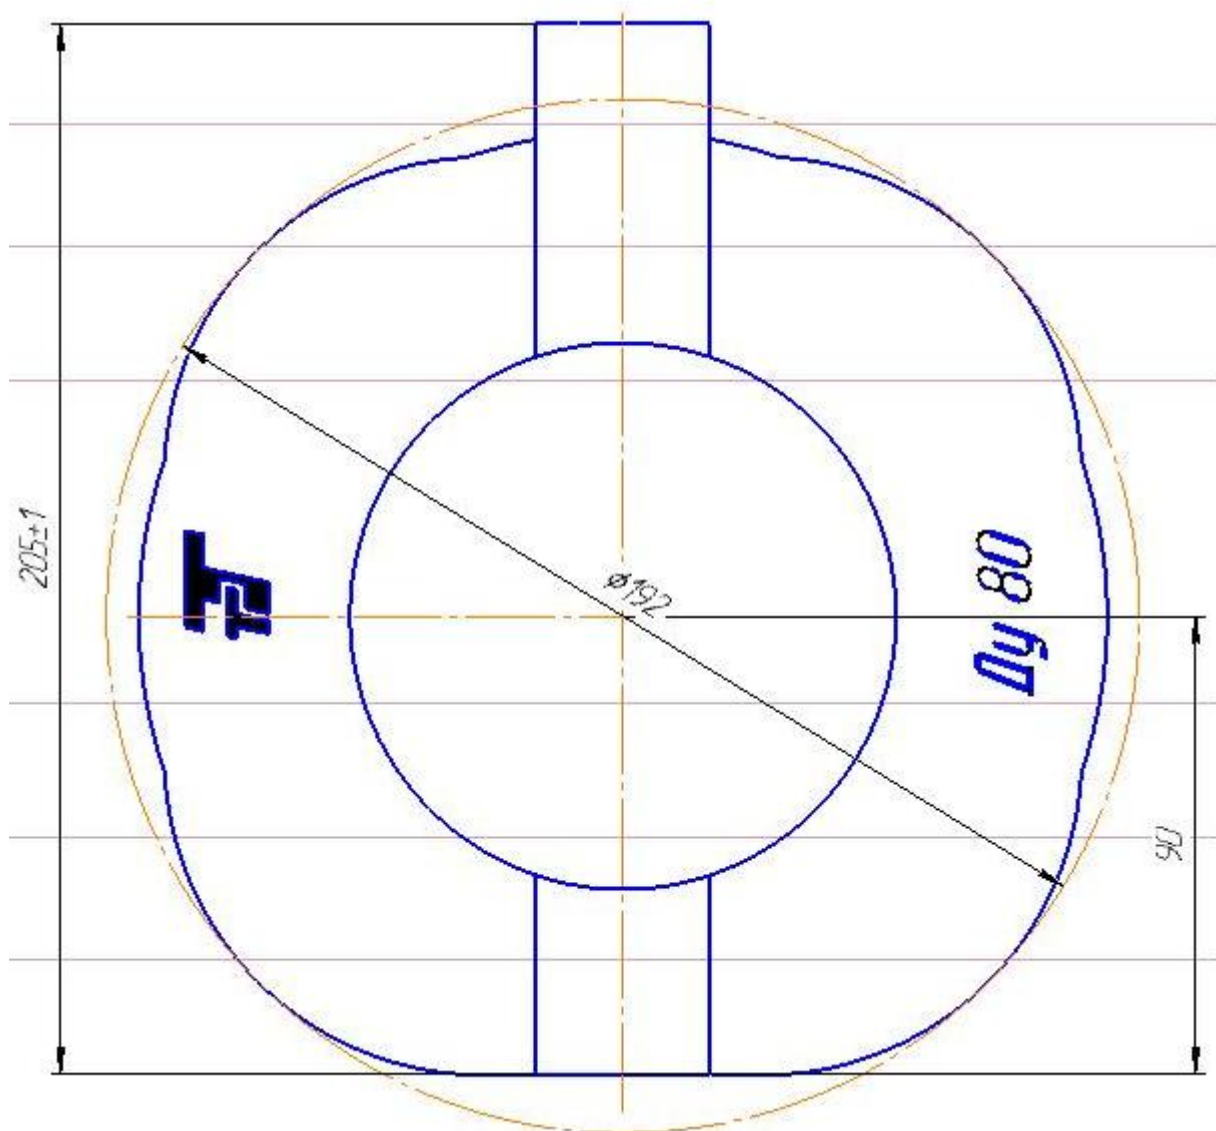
Эскиз заготовки (операция 010 и 015)
